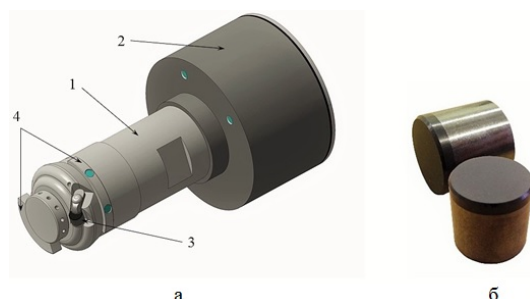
Общий вид режущего измерительного блока (а): 1 – корпус; 2 – электронный блок; 3 – алмазно-твердосплавные пластины; 4 – опорные секторы. АТП (б)
